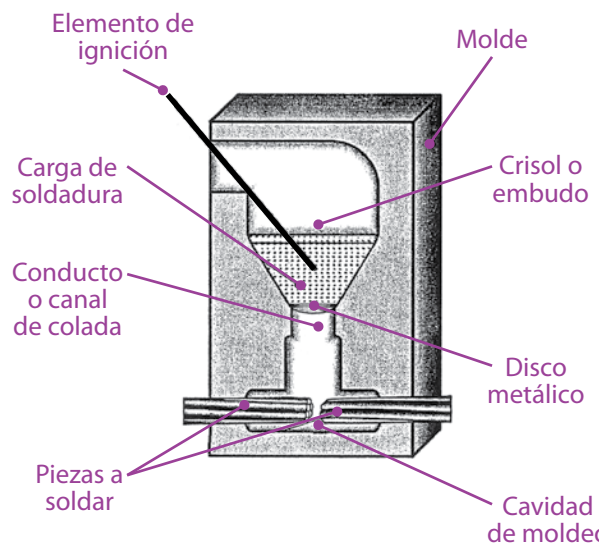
Vista en corte de un molde de soldadura con las piezas a soldarse
